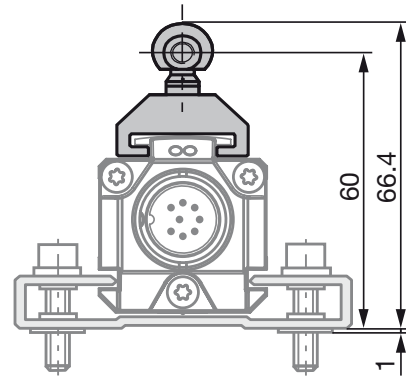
Maße und Abstände mit Positiongeber BTL5-F-2814-1S
